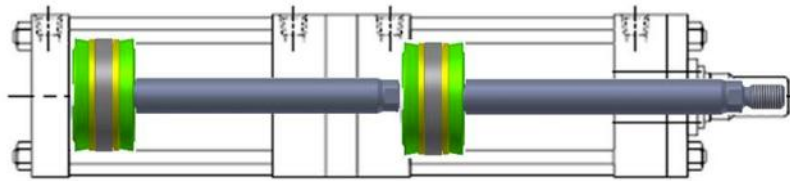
Çift etkili ve çift milli hidrolik silindir yapısı (Hydraulic Cylinder Design, 2025)
